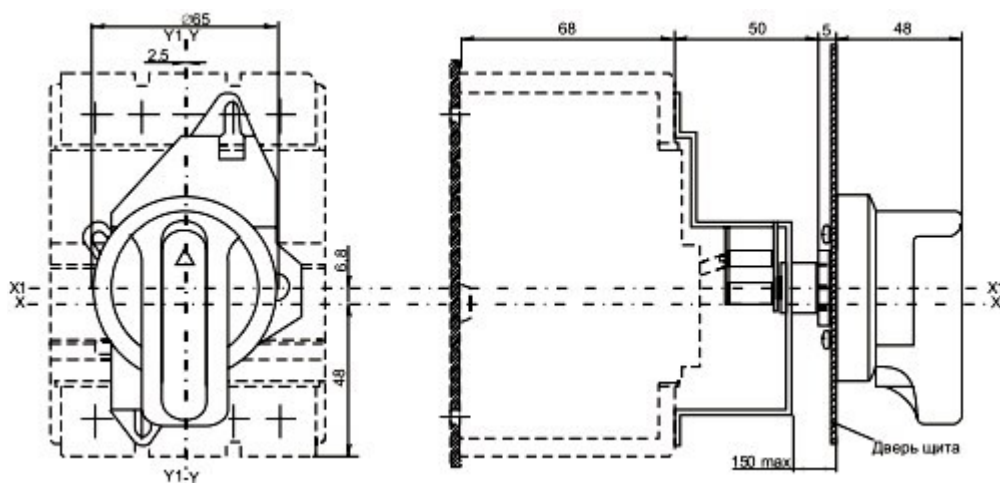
Габаритные размеры выключателя ВА88-32 с ручным поворотным приводом ПРП-32
